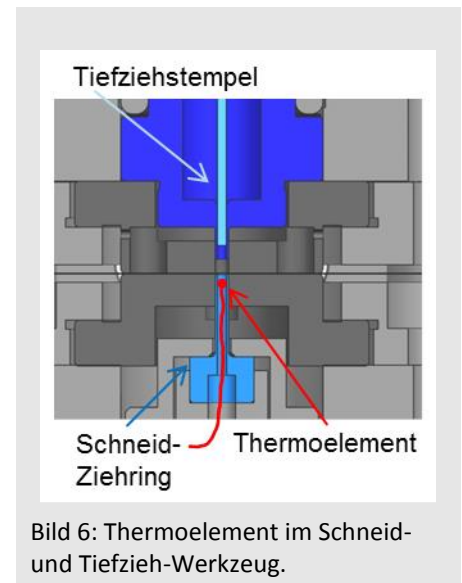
Thermoelement im Schneid- und Tiefzieh-Werkzeug.
